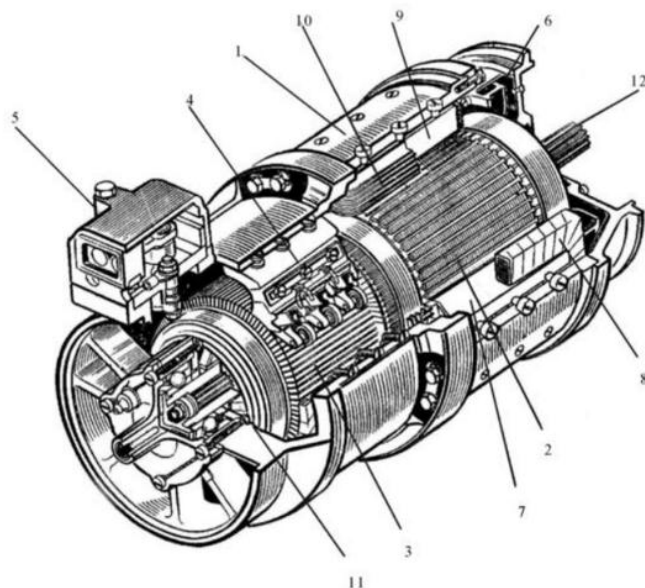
1 – статор; 2 – якорь; 3 – коллектор; 4 – щеткодержатель; 5 – клеммная коробка; 6 – вентилятор; 7 – главный полюс; 8 – обмотка главного полюса; 9 – дополнительный полюс; 10 – обмотка дополнительного полюса; 11 – полый
